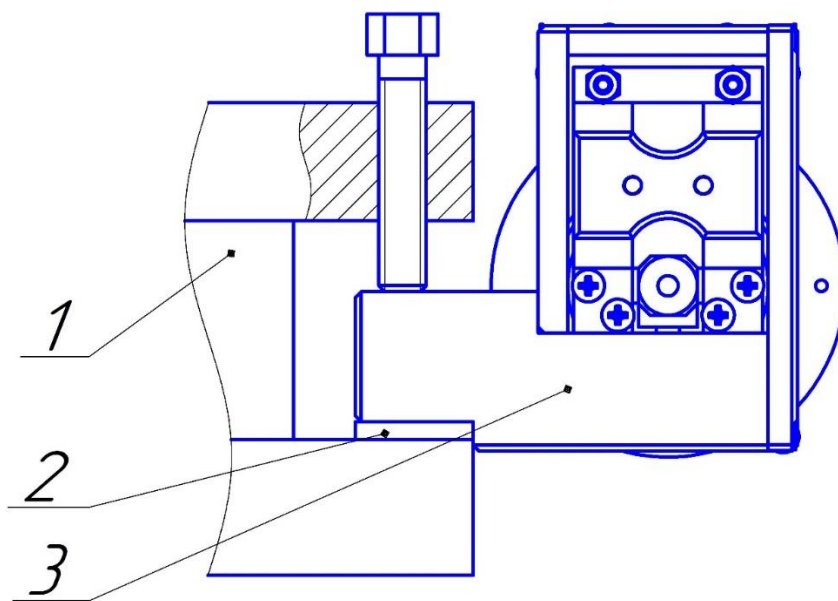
Схема закрепления оправки на токарный станок: 1 – резцедержатель токарного станка, 2 – подкладка, 3 – оправка для алмазного выглаживания
